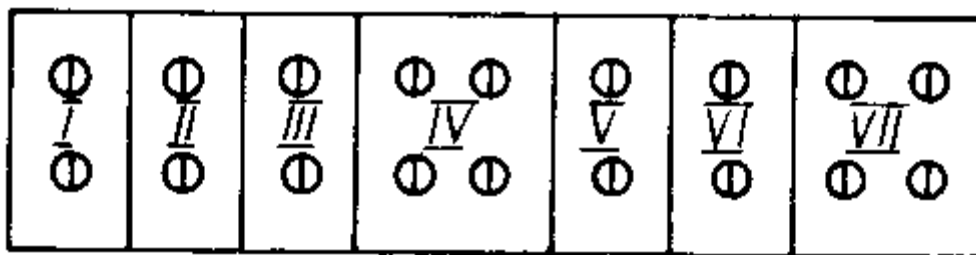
Схема расположения рисок на торцах шпилек крепления коренных подшипников
